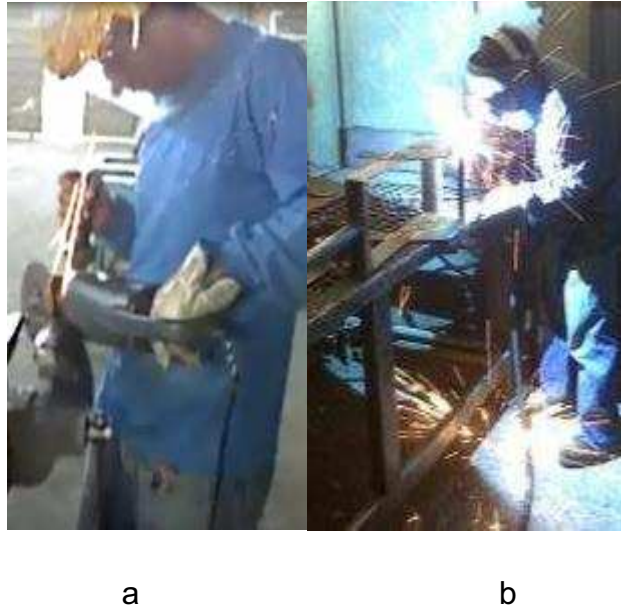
Operaciones tecnológicas: a) Esmerilado; b) Soldadura
